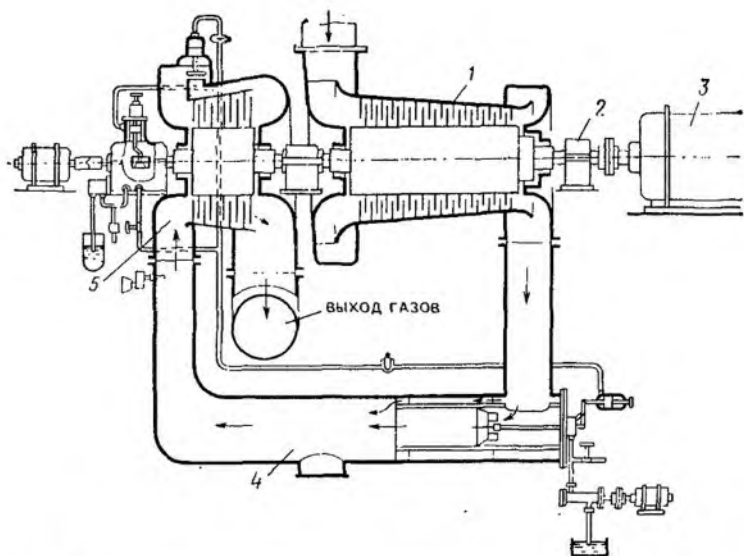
Схема установки осевого компрессора с газовой турбиной
